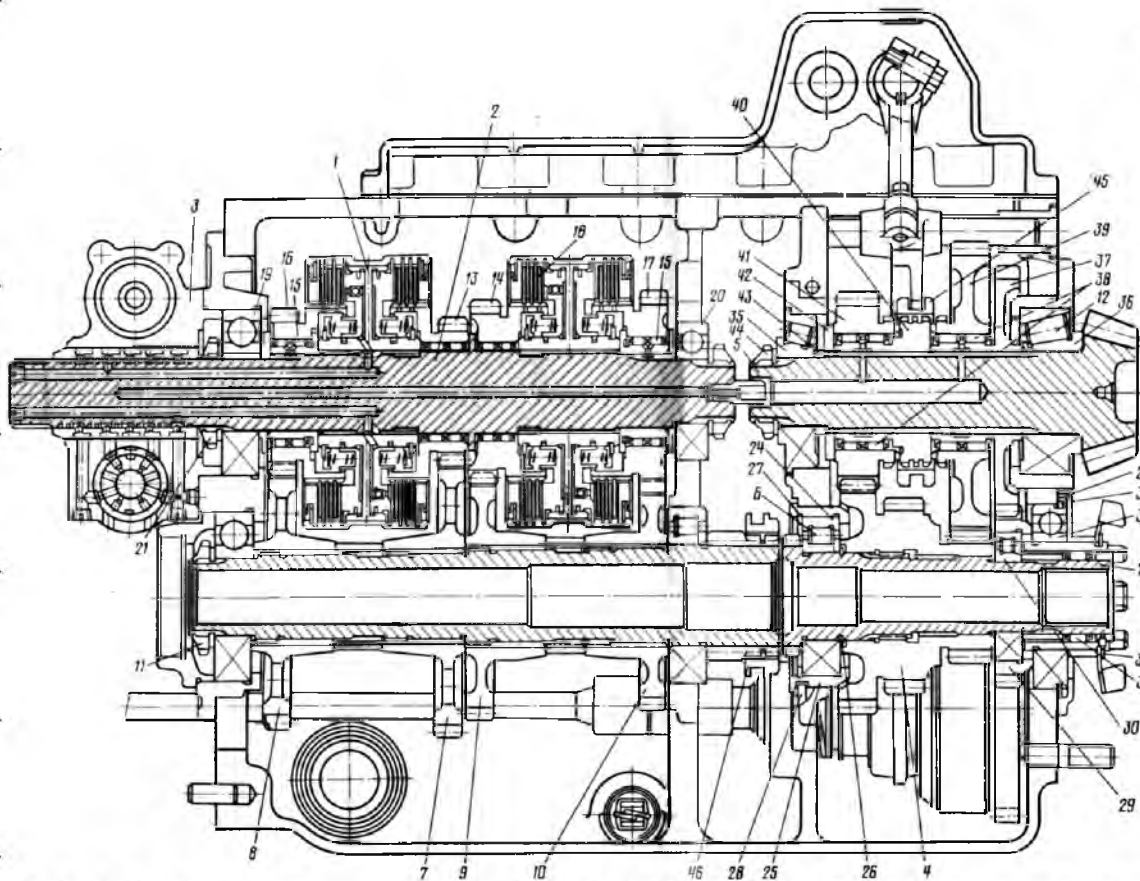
Коробка перемиши передач: 1- вузол передач; 2- первинний вал; 3- розподільник; 4 - блок шестерень; 5 - вторинний вал; 6, 12, 15, 30, 31 і 38 - роликові підшипники; 7 - ведена шестерня I передачі; 8- ведена шестерня передачі; 9 - ведена шестерня II передачі; 10 - ведена шестерня IV передачі; 11, 21 і 44 - гайки; 13 - ведуча шестерня I передачі; 14- ведуча шестерня III передачі; 16 - ведуча шестерня II передачі; 17 - ведуча шестерня IV передачі; багатодискова муфта; 19 20, 24. 32. 35 і 36 - підшипники 22 - стопорна планка; 23 - вал; 25 - стакан 26, 27, 33, 34 - стопорні кільця; 28 - стопорний гвинт; 29 шестерня приводу синхронного ВВП; 37 - ведуча шестерня призода переднього моста і синхронного ВВП; 39 - ведена шестерня першого, другого і четвертого діапазонів; 42 - зубчаста полумуфта; 41 - ведена шестерня третього, п'ятого та шостого діапазонів; 42 - обмежувальна шайба; 43 - регулювальна шайба; 45 - зубчаста рухома муфта; 46 - зубчаста муфта; 47 - вилка перемикач-ня зубчастої муфти
